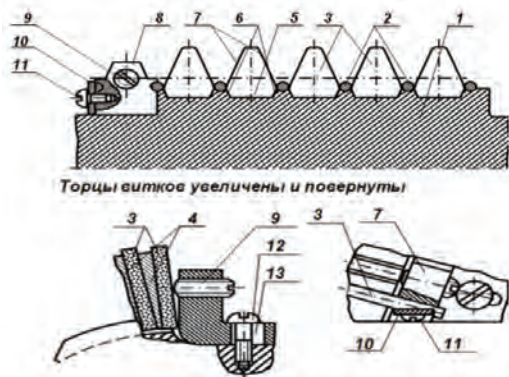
Схема крепления витков, набранных из сменных режущих пластин и клиновых вставок – пружинами, расположенными у ножек между этими витками.
